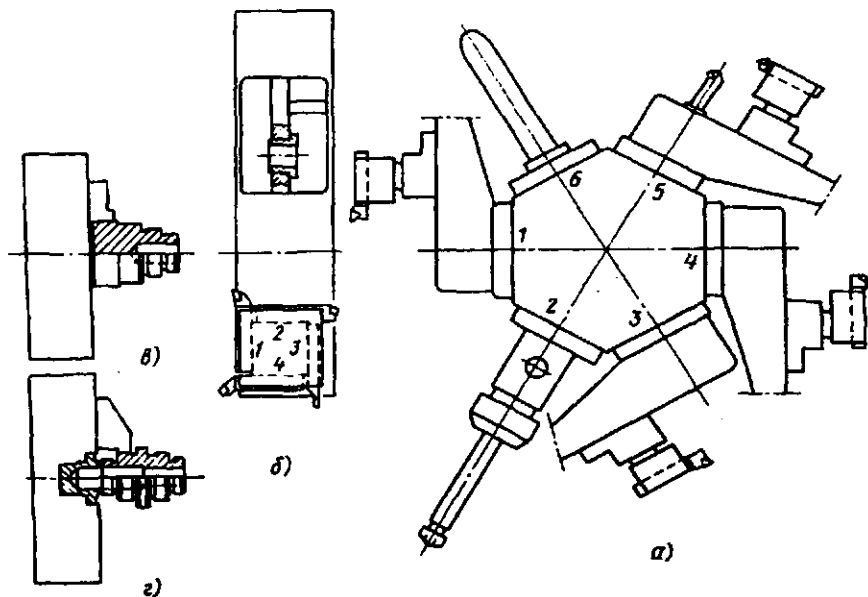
Схемы: а – в – расположения инструмента и закрепления заготовки при сверлении глубокого отверстия; з – закрепления заготовки при сквозном отверстии
